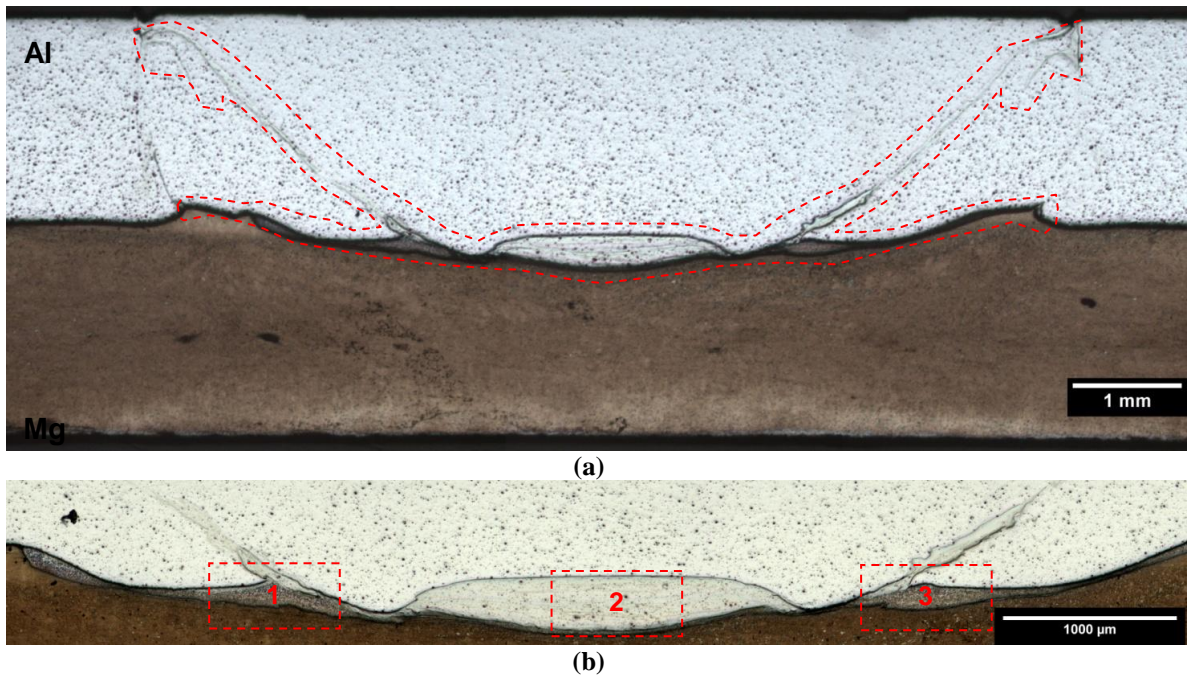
18 Macrografia da solda SpF-Al/Mg, tendo em destaque a camada formada durante o processo de soldagem entre a interface das placas de alumínio e magnésio: (a) 16X e (b) 50X.
